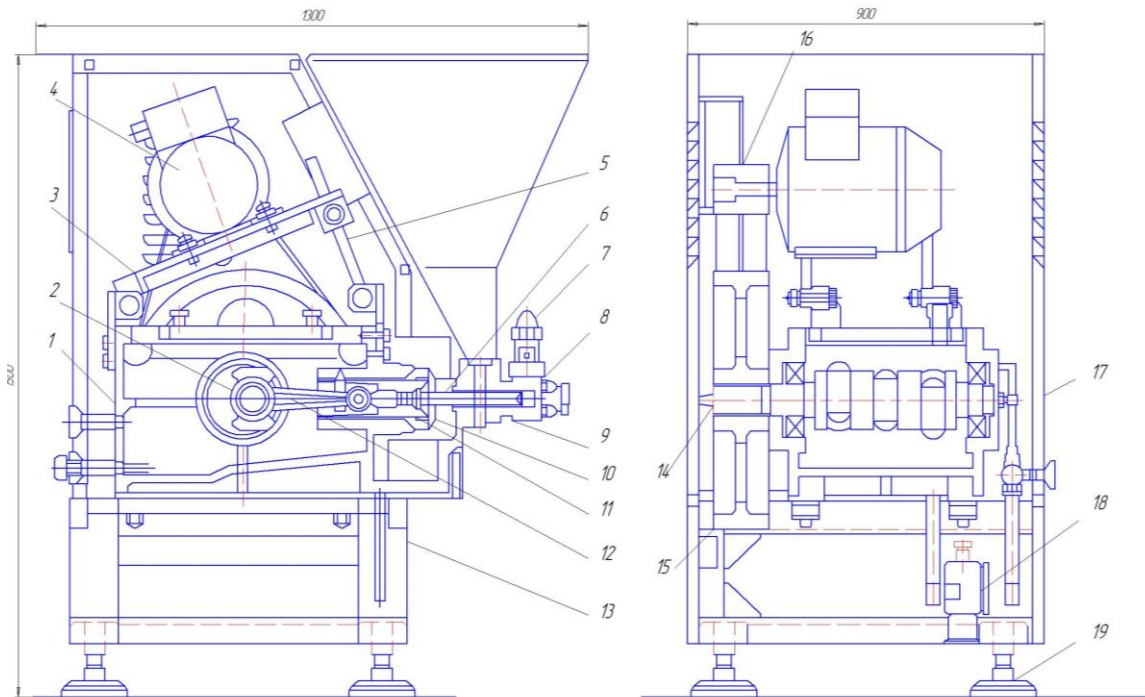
Гомогенізатор А1-ОГ2-С: 1 - кривошипно - шатунний механізм; 2 – кришки шатунів; 3 – підмоторна плита; 4 – електродвигун; 5 – натяжні гвинти; 6 – плунжери; 7 – попереджувальний клапан; 8 – гомогенізуючий пристрій; 9 – плунжерний блок; 10 – ползуни; 11 – пальці; 12 – шатуни; 13 – станина; 14 – колінчастий вал; 15 – ведомий шків; 16 – ведучий шків; 17 – з'їмна кришка; 18 – клинна коробка; 19 – опора.
